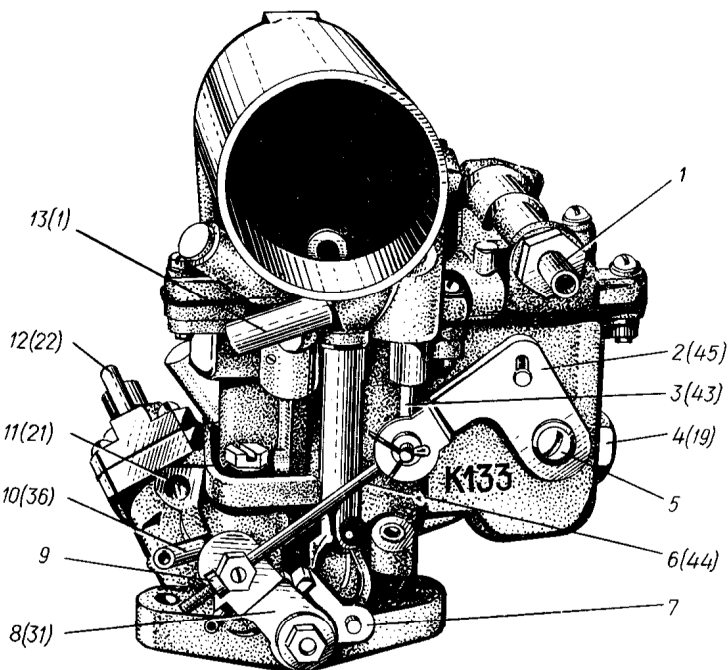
Карбюратор K133; вид сзади (в скобках указаны номера позиций данных деталей на схеме карбюратора (рис. 35):
